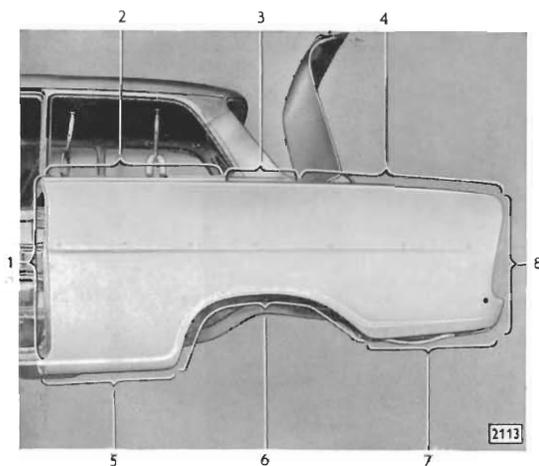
Seitenwand an Karosserie in Einbaulage gebracht und mit Schweißzangen festgespannt
